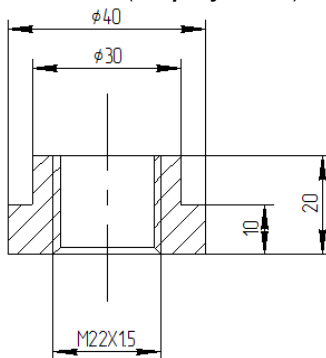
Габаритные и присоединительные размеры патрубка дренажа
